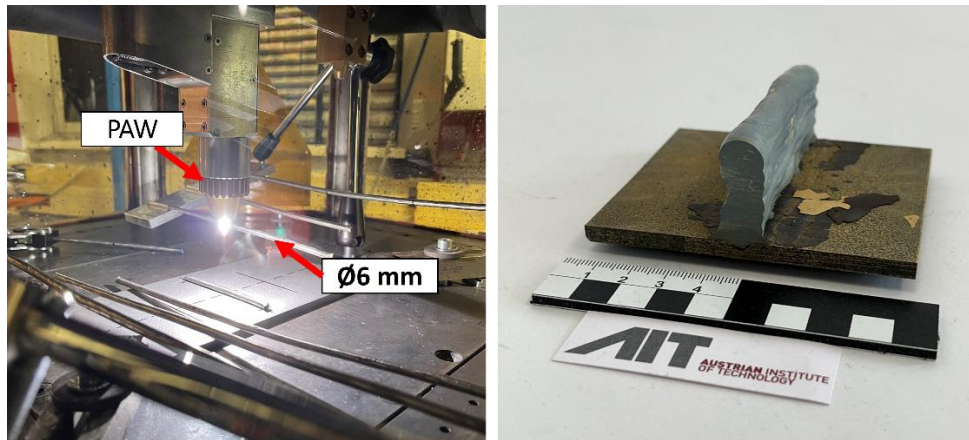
(links) – Versuchsaufbau für die HT12-Bearbeitung (PAW – Plasma-Lichtbogenschweißen); (rechts) – HT12-Abscheidungen.
